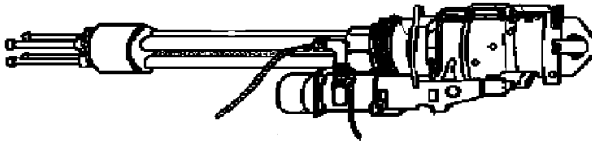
Загальний вид кулемета ГШГ-7,62
